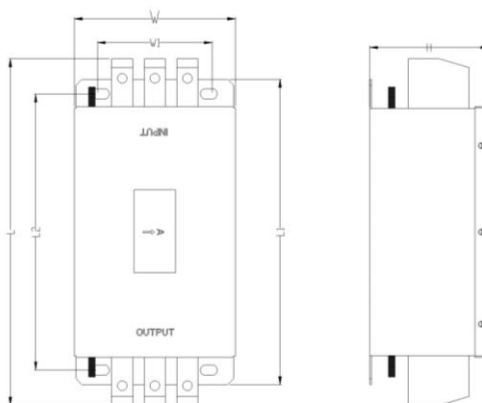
Габаритный чертеж входного волнового фильтра FLT-P04100L-B
